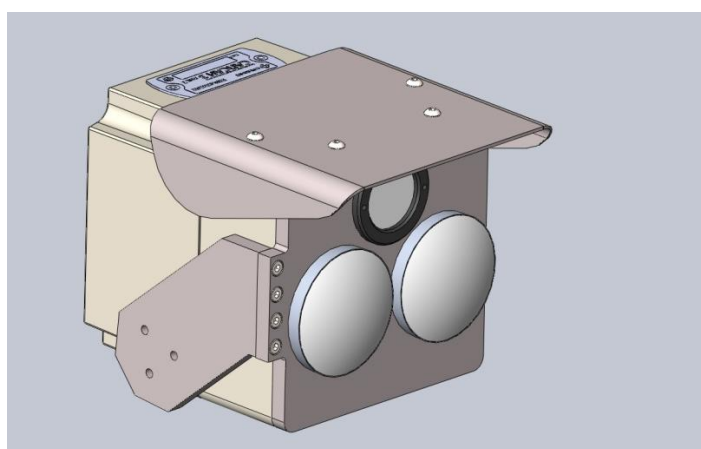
Внешний вид имитатора «Сапсан 3» литера 1 в сборе с безэховой камерой
